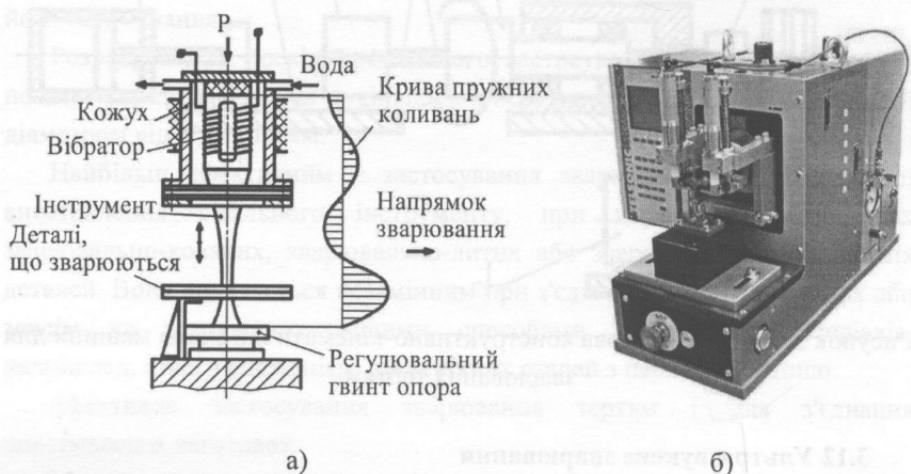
Ультразвукове зварювання: а) – схема здійснення процесу; б) – установка ультразвукового зварювання
